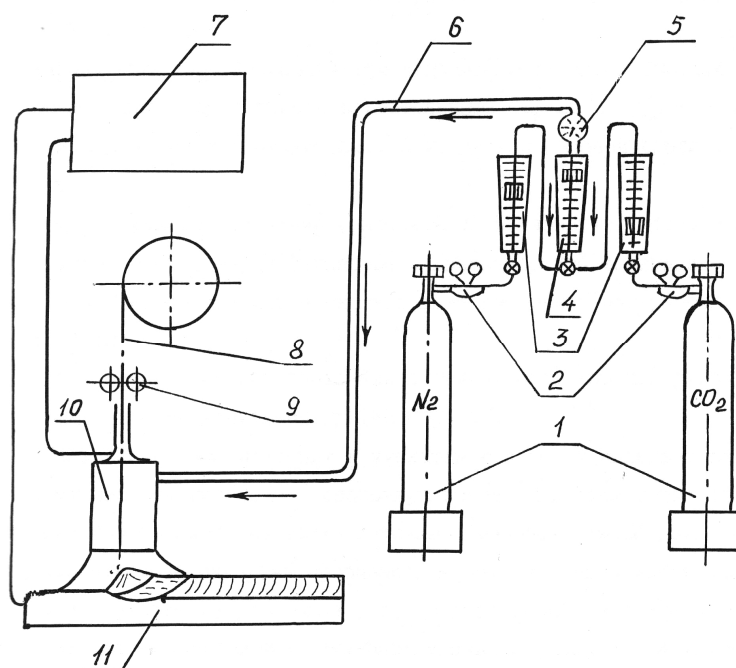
Схема наплавочной установки для технологических исследований: 1 – баллоны с газом; 2 - постовые редукторы; 3 - ротаметры РС-3; 4 - ротаметр РС - 3А; 5 - манометр; 6 - шланг подачи защитной атмосферы; 7 - сварочный выпрямитель; 8 - наплавочная проволока; 9 - подающий механизм проволоки; 10 - газозлектрическая горелка; 11 - наплавляемая пластина
